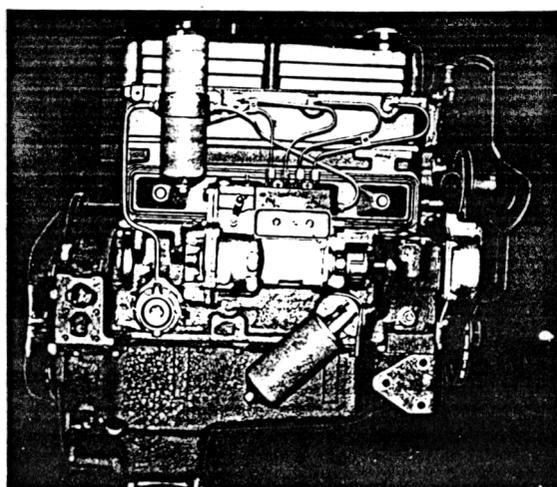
A-01-04 - Vista del lado derecho del motor EBR0
